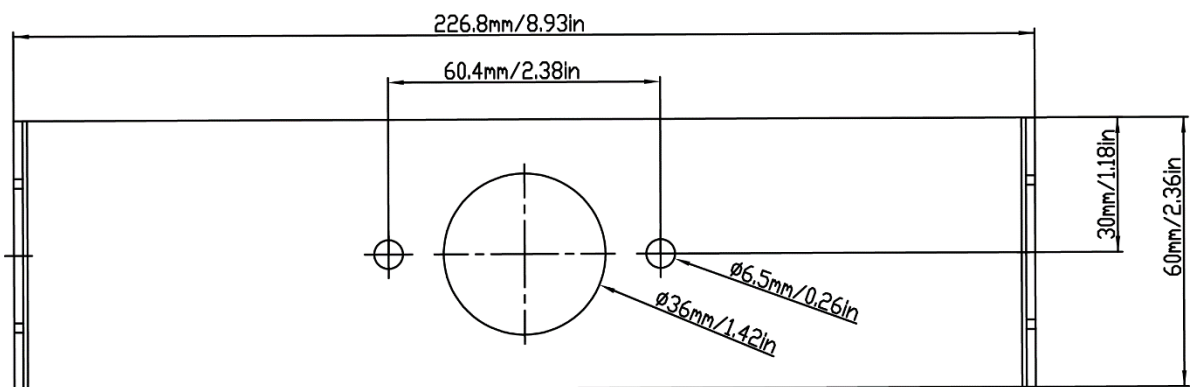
Dimensioni della staffa di montaggio dell'i-DT33XW
